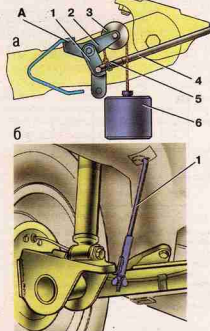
Регулировка привода регулятора давления: а) 1 – шаблон; 2 – рычаг приспособления; 3 – ролик; 4 – рычаг привода регулятора давления; 5 – скоба; 6 – груз; А – упор рычага; б) 1 – штанга
